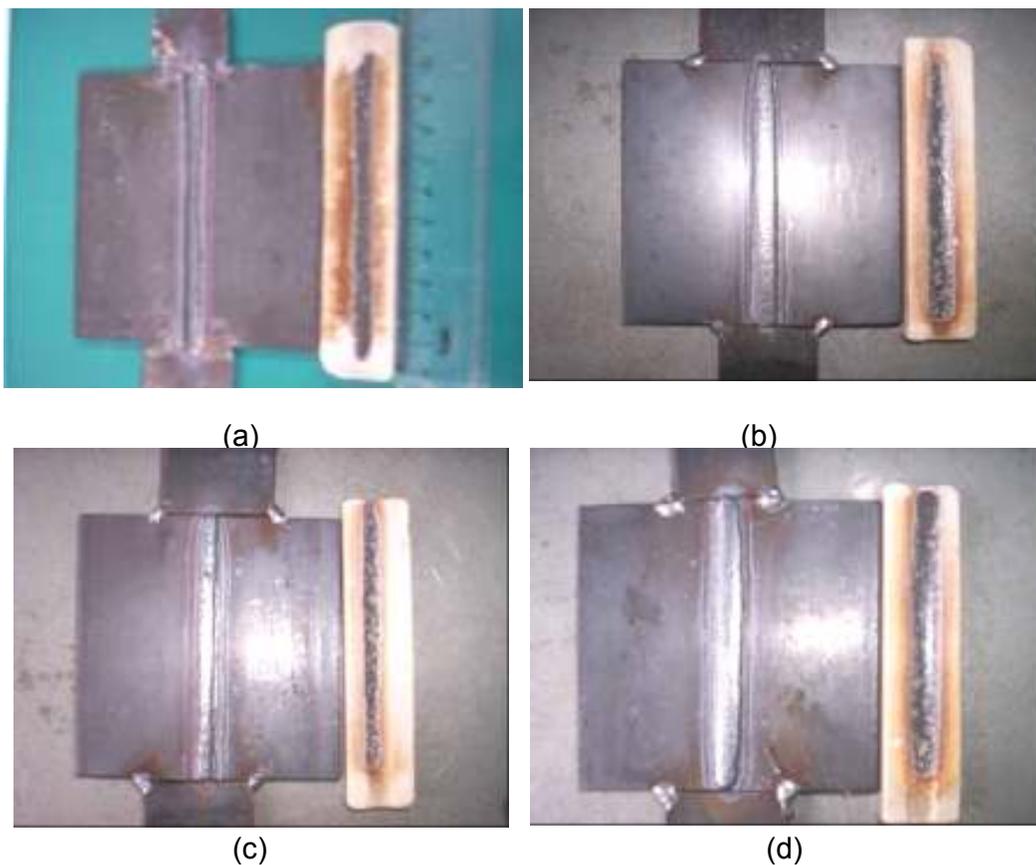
Corpos de prova dos suportes cerâmicos produzidos após a soldagem
